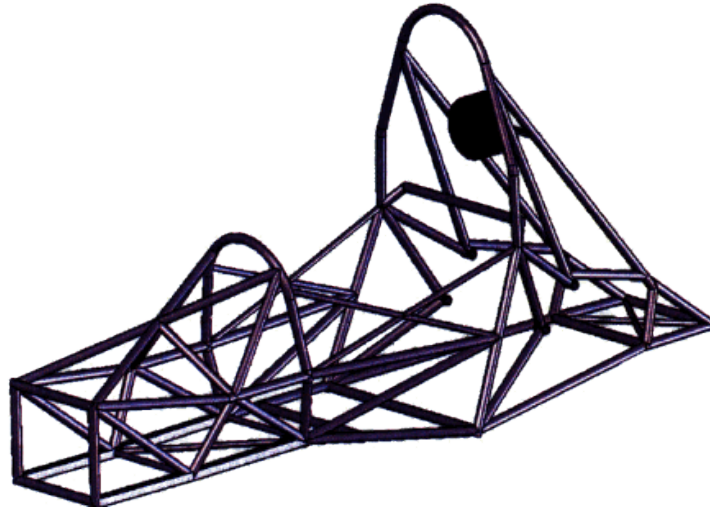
Chassi tubular tipo space frame. Fonte: Technical F1 Dictionary.
